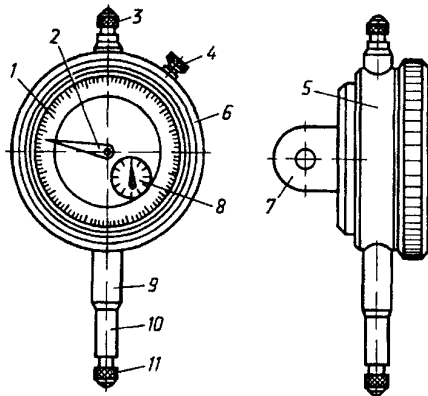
Індикатор годинникового типу: 1 - шкала; 2 - стрілка; 3 - головка вимірювального штифта; 4 - стопор; 5 - корпус; 6 - ободок; 7 - вушко; 8 - показчик кількості обертів; 9 - гільза; 10 - вимірювальний штифт; 11 - наконечник
